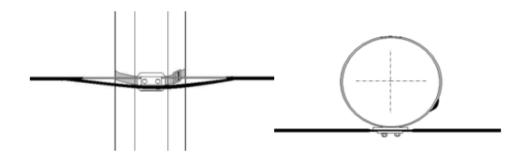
FIGURA CON VISTA FRONTAL Y VISTA DE PLANTA CON HERRAJE TIPO SUSPENSIÓN Fuente: Lineamientos Técnicos y Administrativos del SEN año 2014
